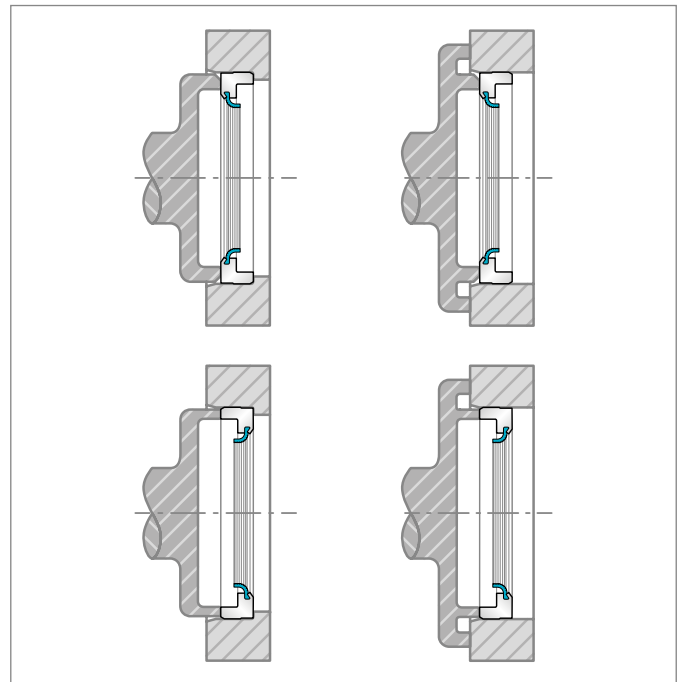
Montagewerkzeuge für das Einpressen in Gehäuse
